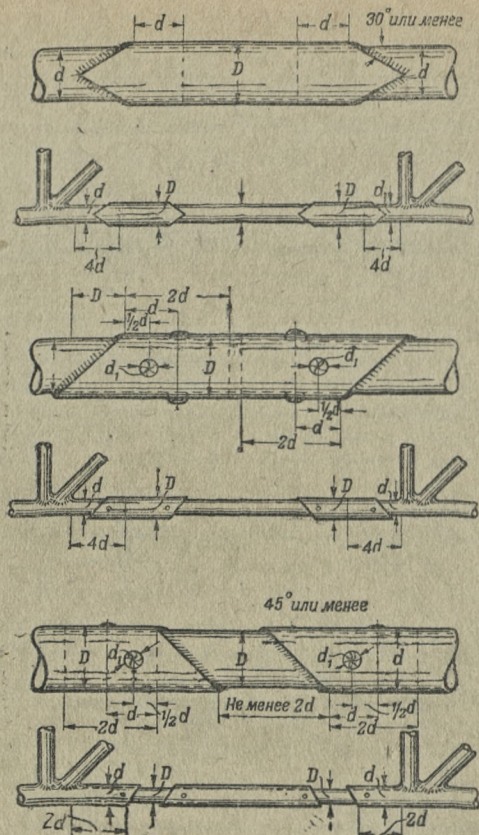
Примеры ремонта сварных конструкций самолета постановкой наружных и внутренних бужей
